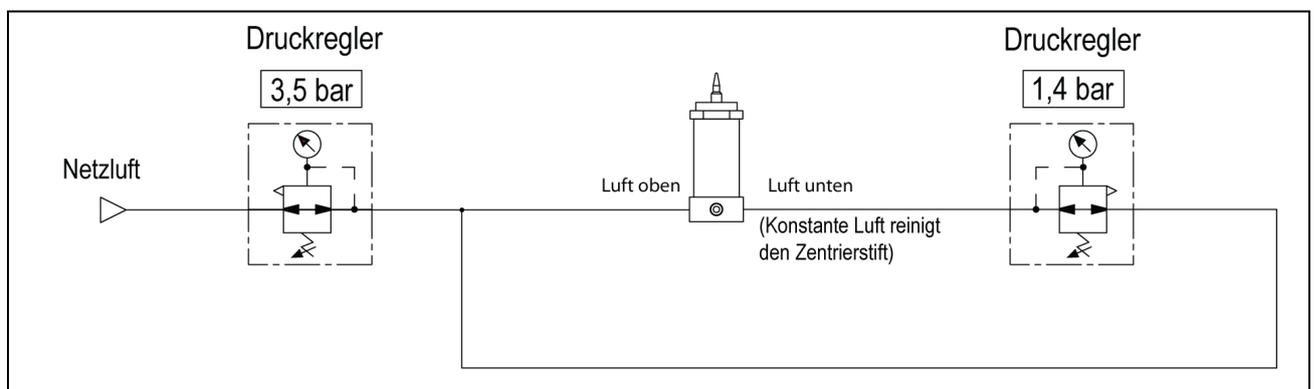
Pneumatisches Anschluss-Schema für LVDT Schweisskörper mit nicht einziehbarem Zentrierstift (nicht möglich bei geklemmter Ausführung)
